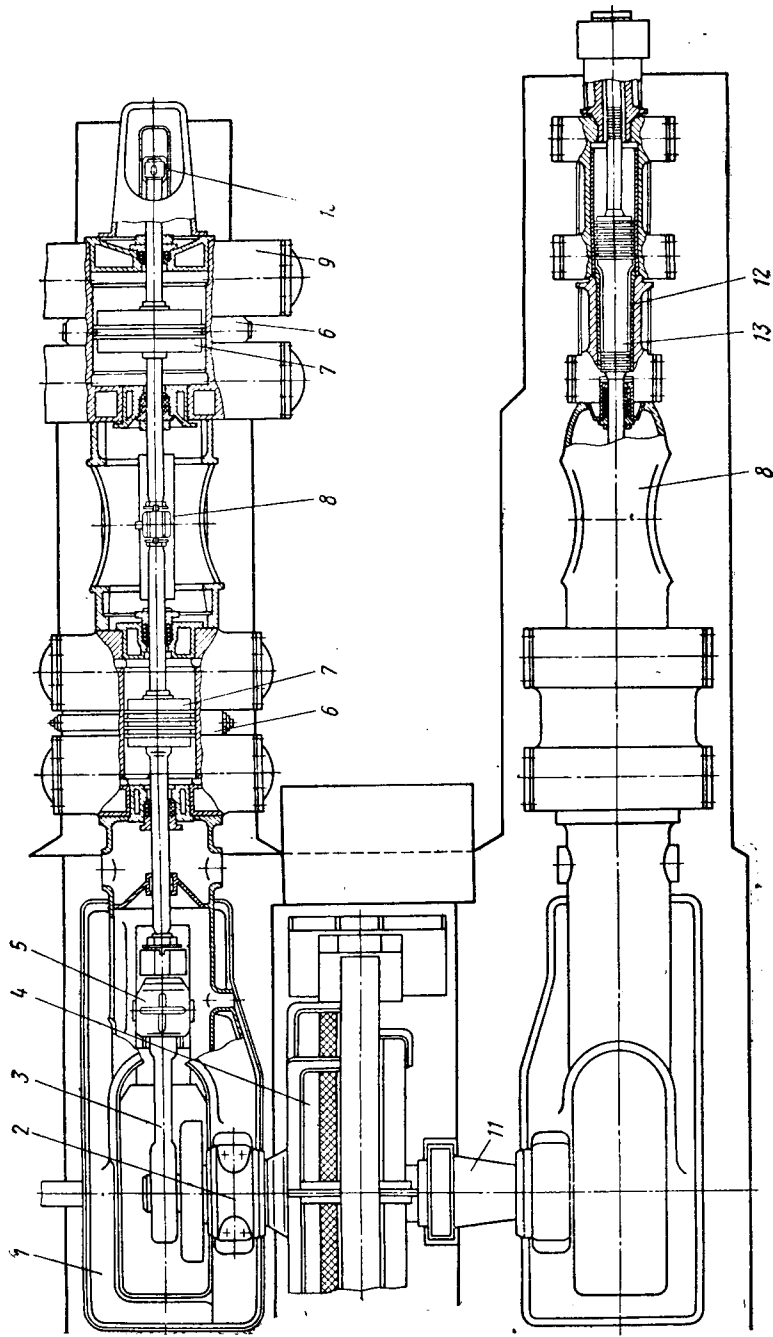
Горизонтальный двухрядный многоступенчатый компрессор с односторонним расположением цилиндров:
